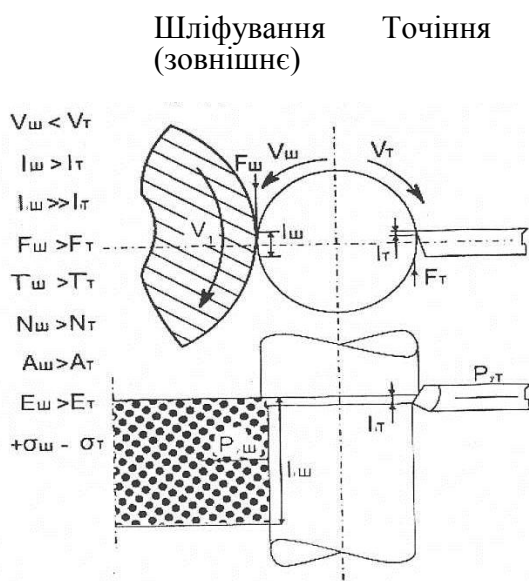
Схема контакту інструменту з оброблюваною поверхнею при шліфуванні і точінні
